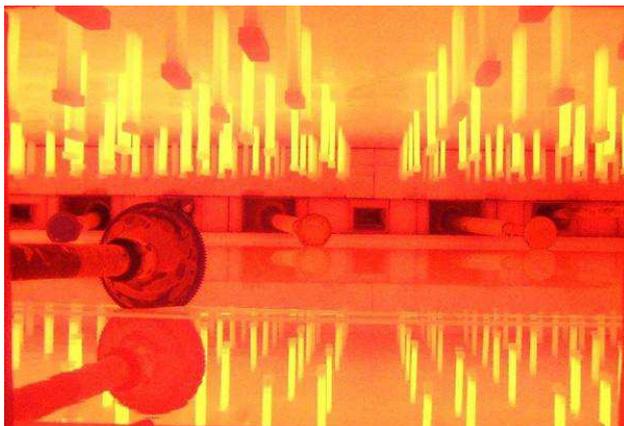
Foto interna do Tin Bath ou banho de estanho.
